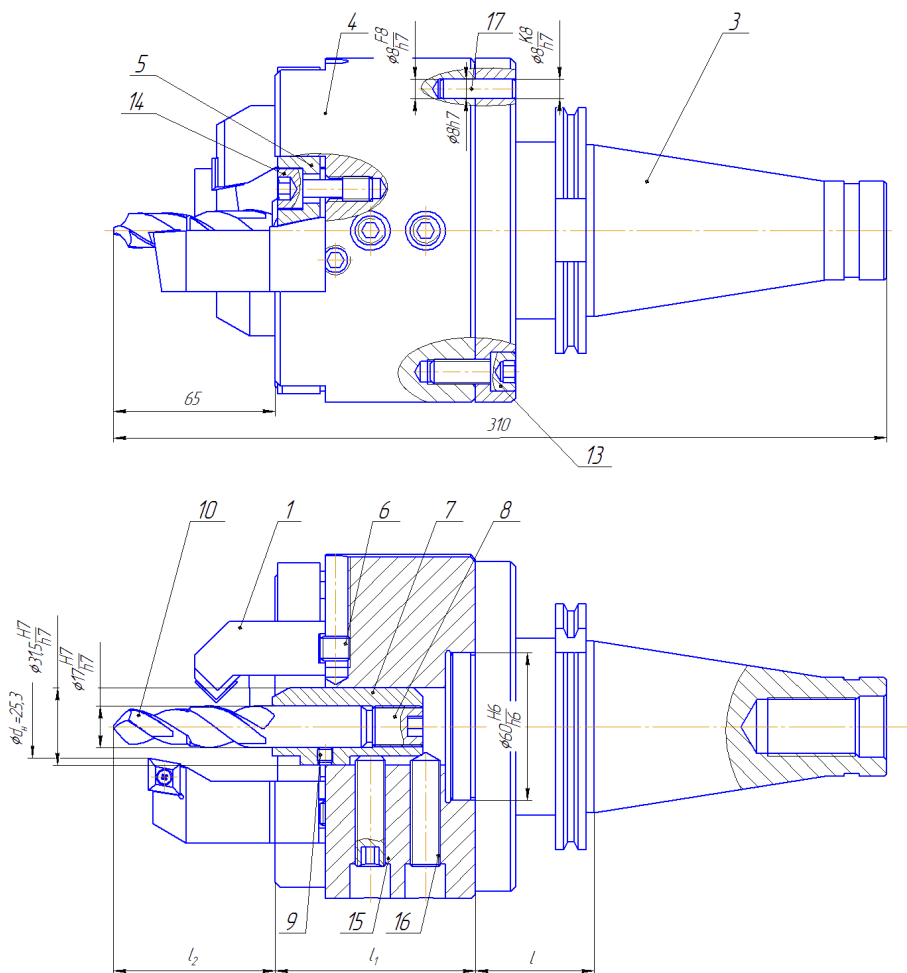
Конструкція збірного комбінованого інструменту:
